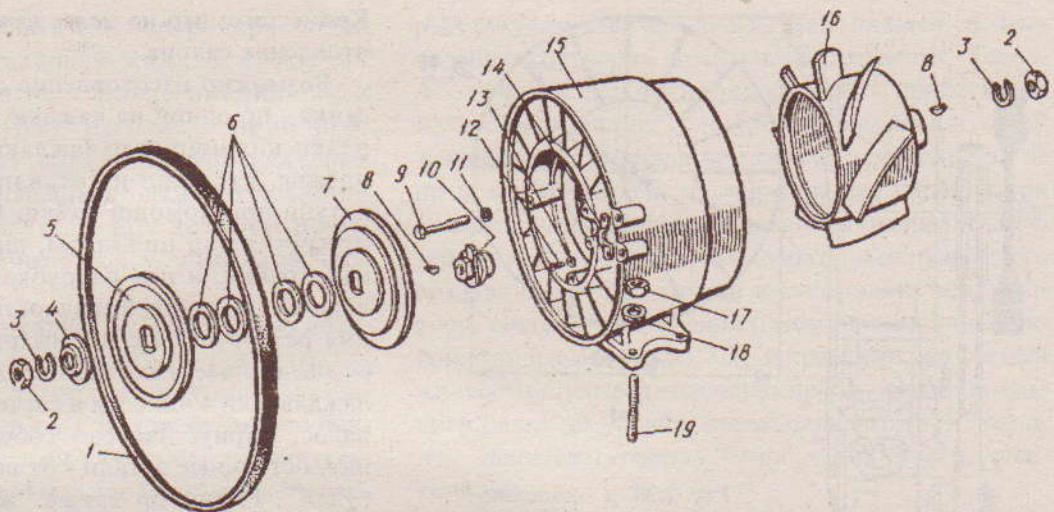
Вентилятор охлаждения двигателя: 1 - ремень I-8,5x8-1018; 2 - гайка М16; 3 - шайба 16Л; 4 - колпачок нажимной шкива вентилятора; 5 - половина шкива вентилятора передняя; 6 - шайба регулировочная; 7 - половина шкива вентилятора задняя; 8 - шпонка 4x6,5; 9 - болт М6; 10 - ступица; 11 - шайба 6 стопорная; 12 - винт М5; 13 - шайба 5; 14 - скоба крепления проводов; 15 - аппарат направляющий; 16 - колесо; 17 - гайка М8; 18 - шайба 8; 19 - шпилька М8
